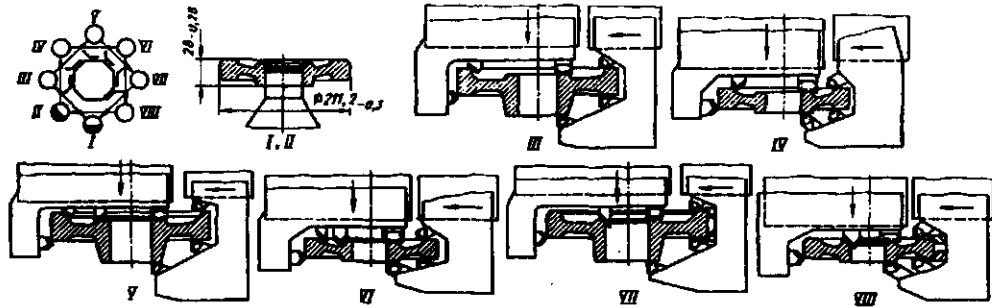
Наладка восьмишпиндельного полуавтомата для обработки двух различных заготовок зубчатых колес
